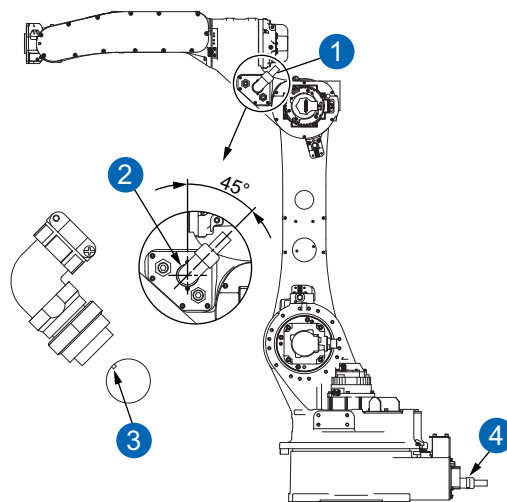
Gegenstecker für den internen Kabelbaum (Ellenbogen-Typ)
